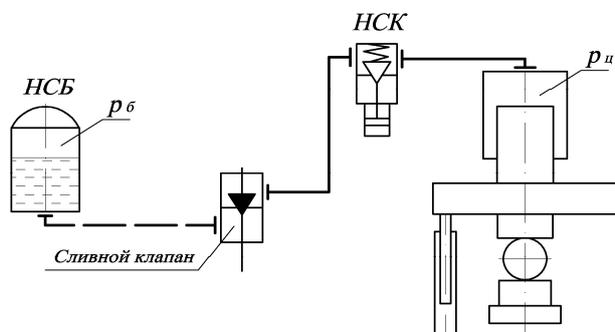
Схема разгрузки рабочего цилиндра сливным клапаном небольшого сечения, встроенным в главный клапанный распределитель
